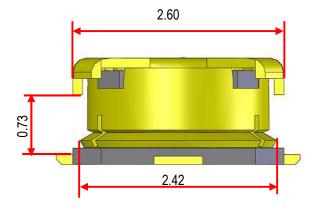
抜去 JIG 引っかけ形状配置図(PLUG connector design feature to hook pull jig)
